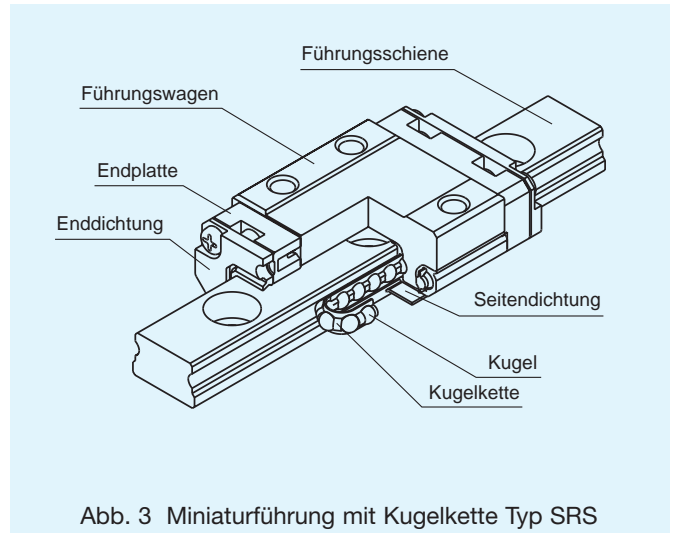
Miniaturführung mit Kugeldette Typ SRS
